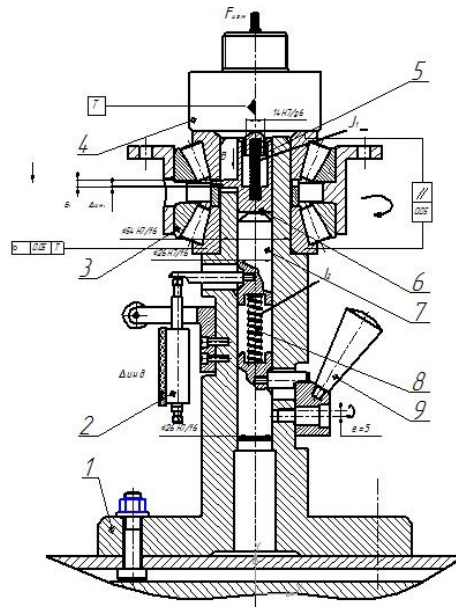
Технологическая установка для контроля момента трения в дуплексе подшипников перед преднатяга регулированием (1 — корпус, 2 — фальш-оправка, 3 — контролируемый подшипниковый узел, 4 — ведомый диск, 5 — показывающий прибор-манометр, 6 — микрометр подвода, 7 — пневмотурбина, 8 — ведущий вал с отверстием для подвода воздуха к форсунке, 10 — поводковый палец)
